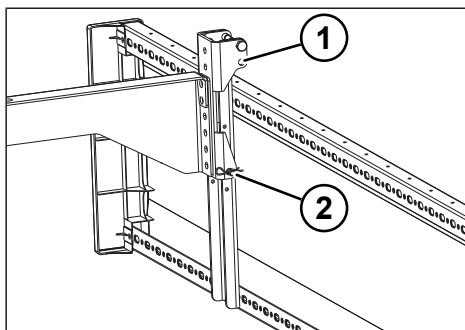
Dispositivo di protezione laterale abbassato (vista lato posteriore))
